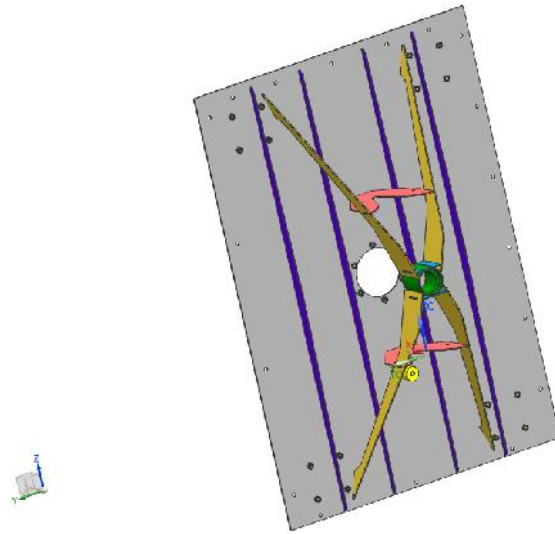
Der Rahmen des Pumpenprüfstandes
